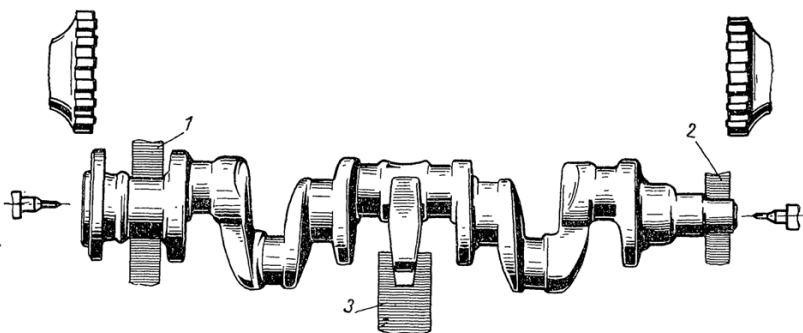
Схема ориентирования заготовки коленчатого вала при фрезеровании и центровании торцов:
